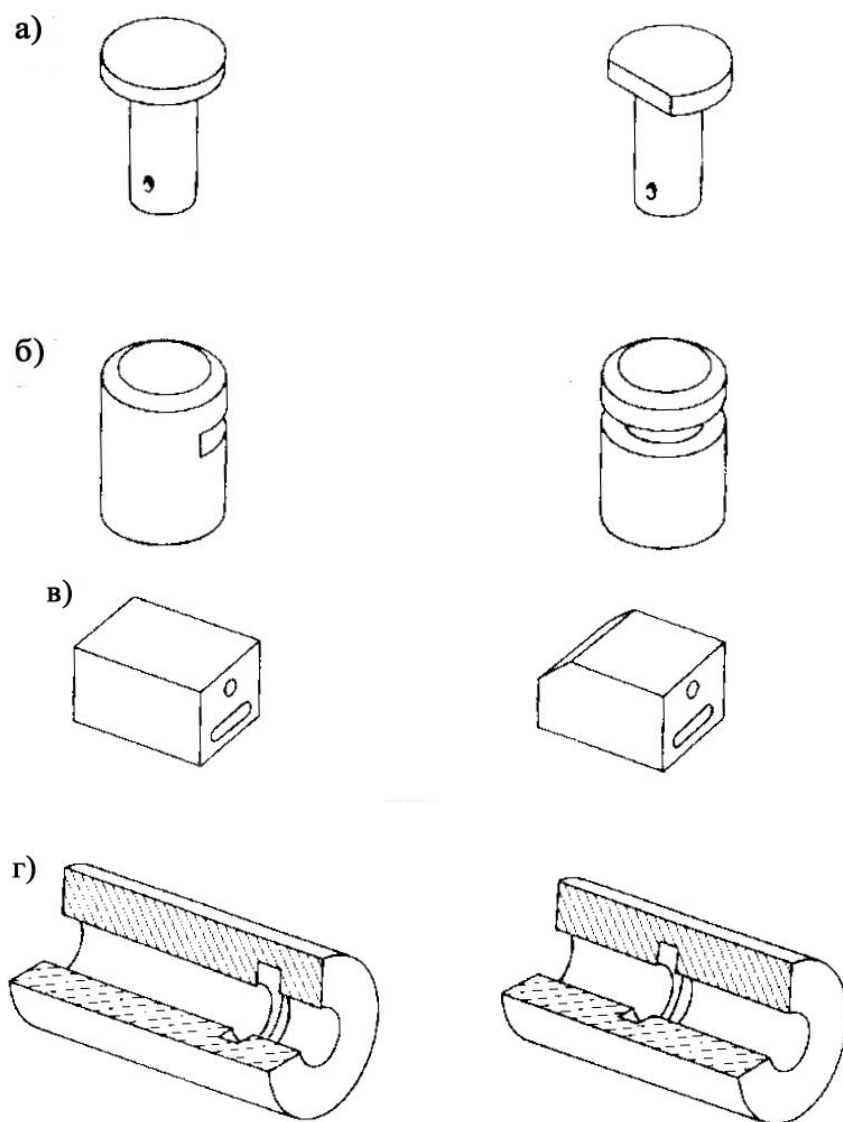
Отличительные конструктивные признаки для ориентации и распознавания деталей
